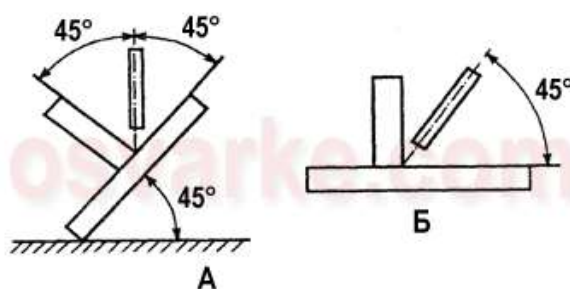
Техника выполнения угловых швов при ручной дуговой сварке:
